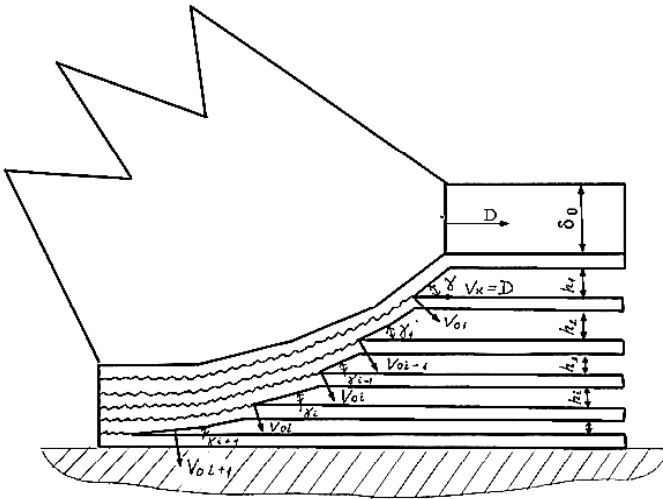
Схема пакетного способа сварки взрывом [24, 28]
